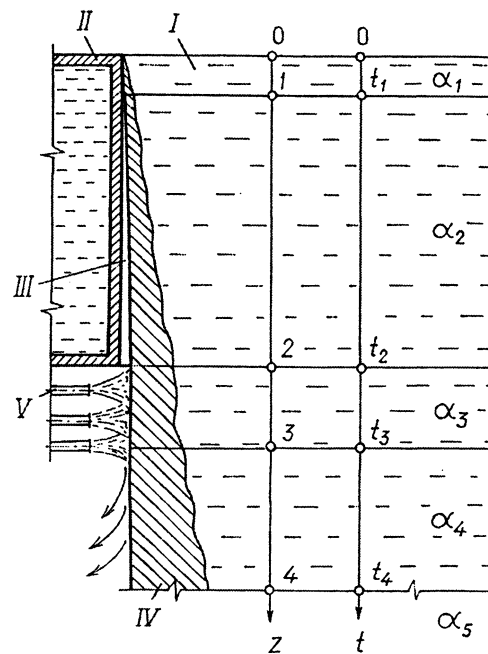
Схема расположения расчетных зон в начальной стадии формирования непрерывнолитой заготовки: I – расплав металла; II – стенка кристаллизатора; III – газо-воздушный зазор; IV – твердая корка литой заготовки; V – форсунка водяного охлаждения
